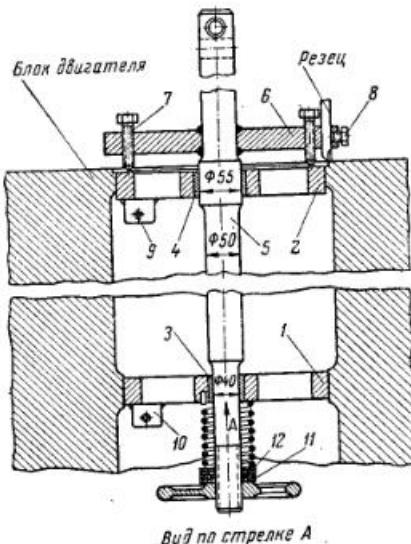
Приспособление для проточки посадочных поясков в блоке цилиндров:
